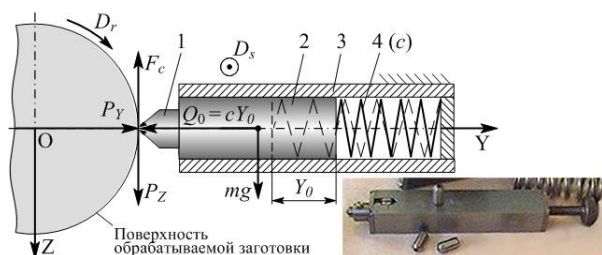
Схема обработки цилиндрической заготовки методом ППД инструментом упругого действия: 1 – вставка с индентором; 2 – ползун; 3 – корпус инструмента; 4 – пружина сжатия
